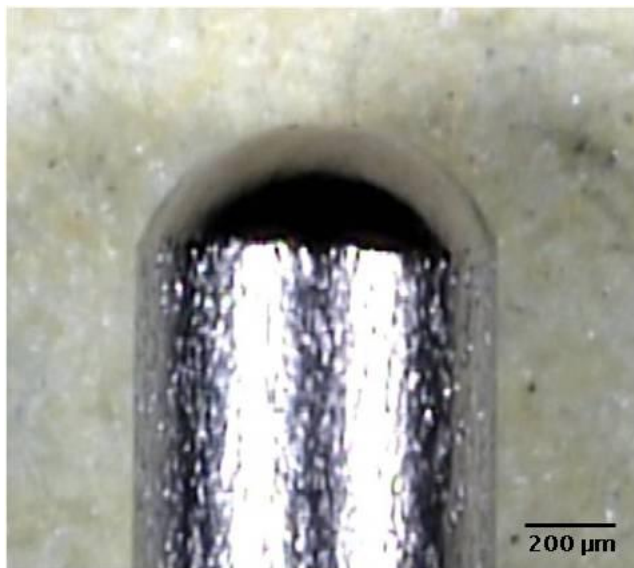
Tubo de titânio soldado com potência de pulso de laser adequada apresentando região da solda simétrica e esférica ( $P_p=1,0$  kW)
